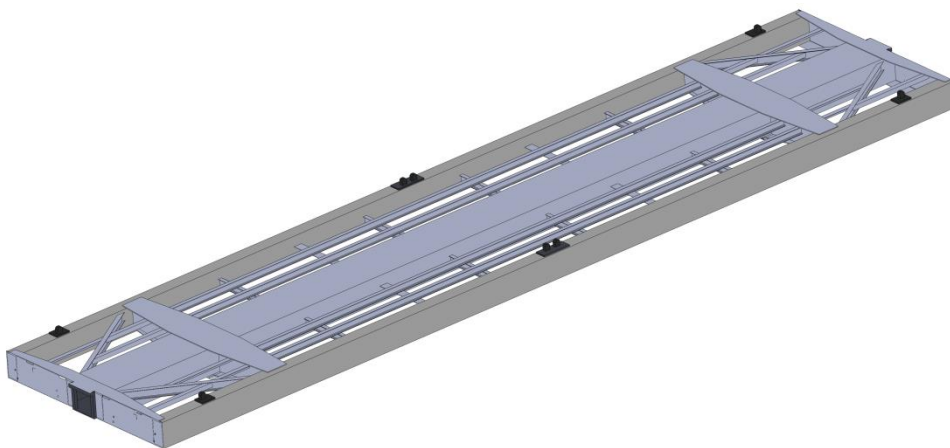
Просторова модель несучої конструкції вагона-платформи
